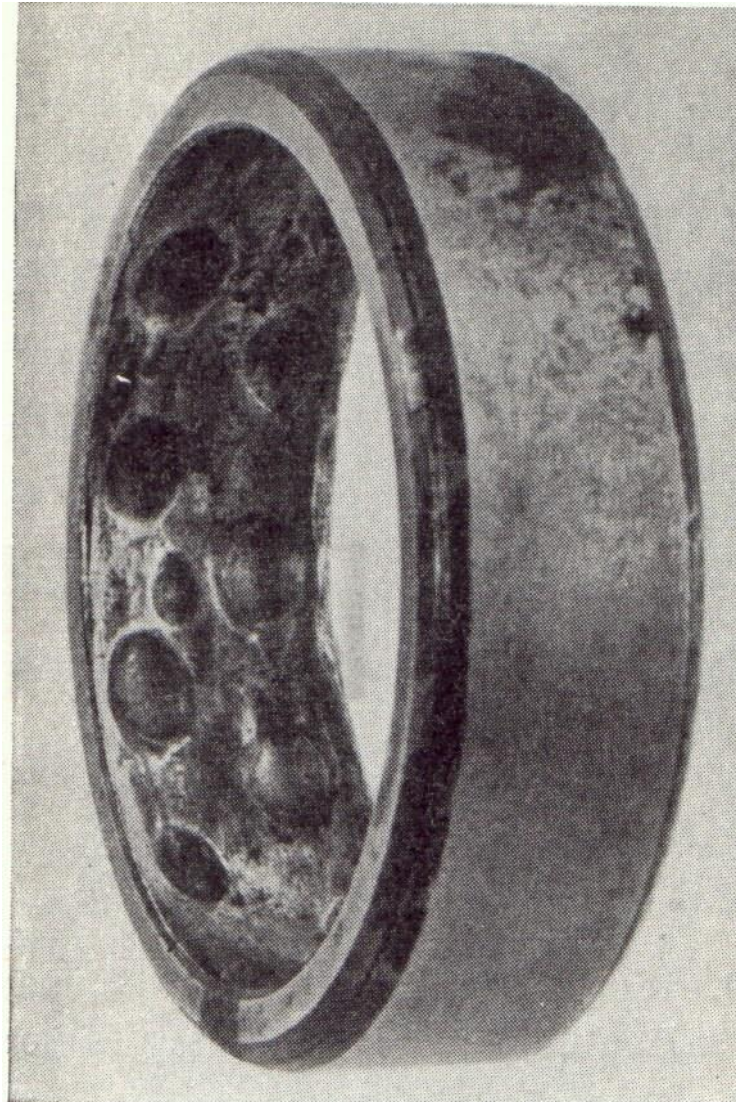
marcas por corrosión por vibración en la pista de rodadura externa de un rodamiento de bolas a rótula [2].
